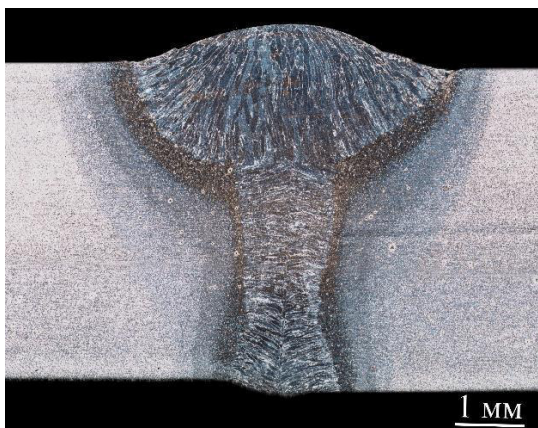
Структура сварного шва стали 09Г2С, полученного методом гибридной лазерной сварки
